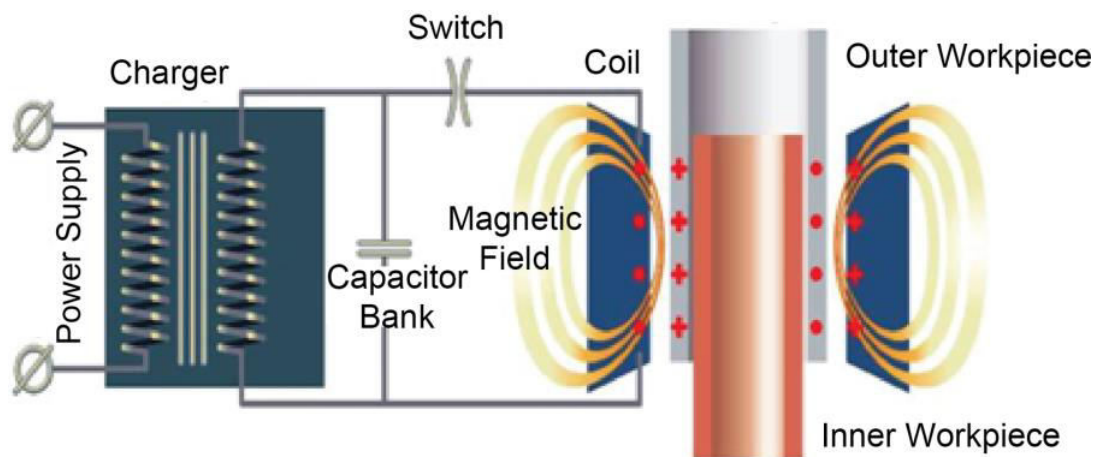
Principe de Soudage par Impulsion Magnétique
